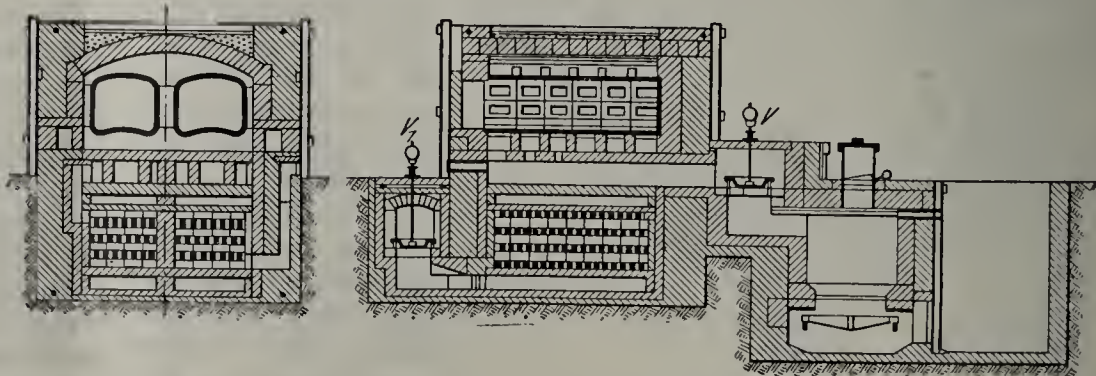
Zwillingmuffelofen mit Gaserzeuger und Regenerator.
